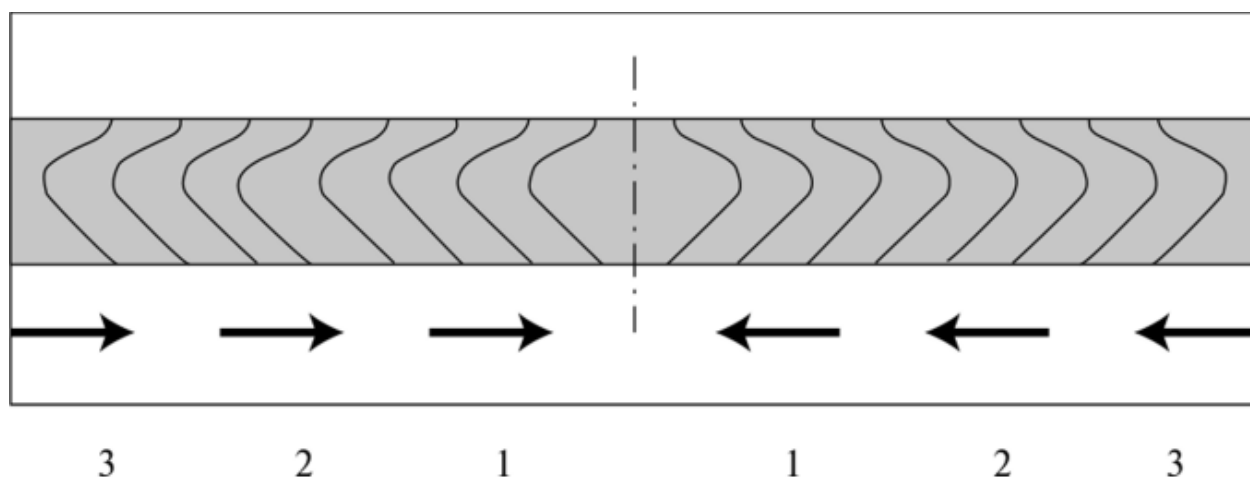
Разбивка сварочного шва на участки при сварке
